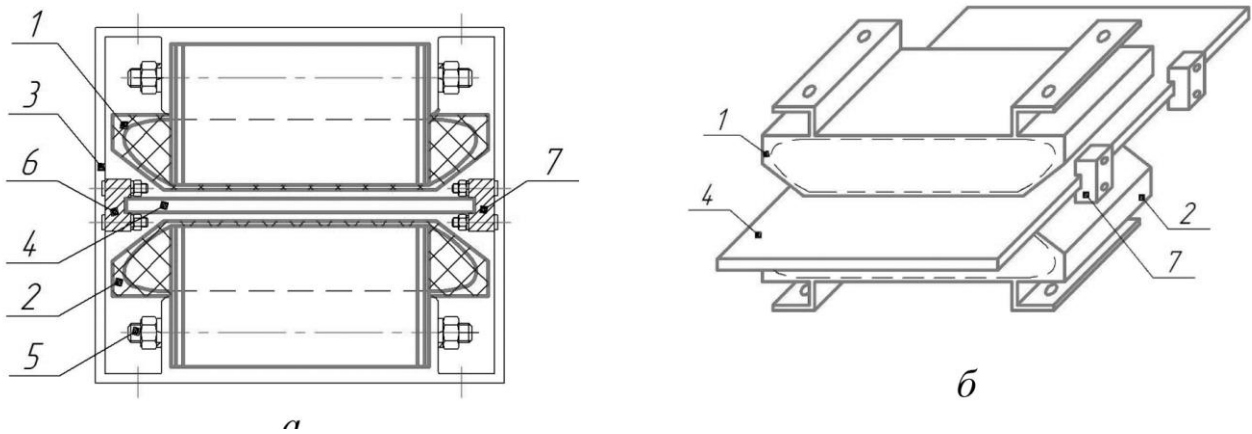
Конструкція розроблюваного ДПЛАД: а – поперечний розріз ДПЛАД; б – розташування елементів ДПЛАД (без корпусної оболонки); 1 – верхній індуктор ДПЛАД; 2 – нижній індуктор ДПЛАД; 3 – корпус ДПЛАД; 4 – вторинний елемент ДПЛАД; 5 – кріпильно-регулювальні болти індукторів; 6, 7 – фторопластові підшипники ковзання [1].
